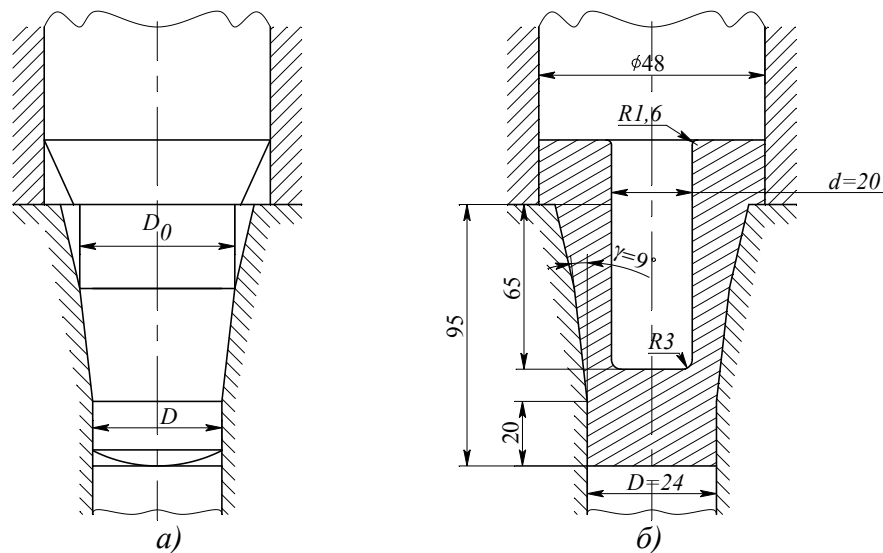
Переходы штамповки поковки конического стакана с цилиндрической полостью
